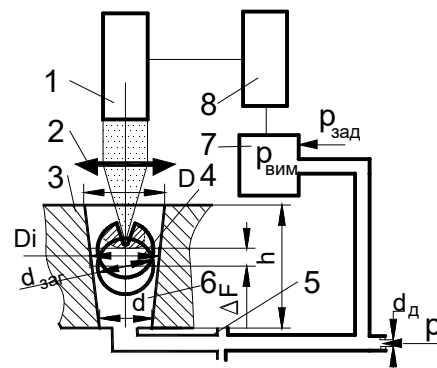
Лазерна установка для обробки конусних отворів (1 – лазер, 2 – об'єктив, 3 – стіл з отвором для утримання заготовки 4 під час обробки, 5 – штуцер для подачі повітря, 6 – отвір для розташування заготовки, 7 – чутник пневматичний, 8 – блок керування лазером)
